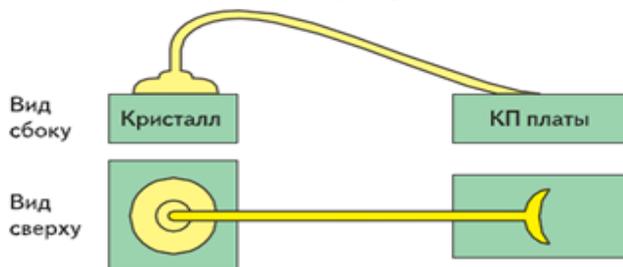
Профиль проволочного контакта, выполненного по технологии термозвуковой сварки «шарик-клин»
